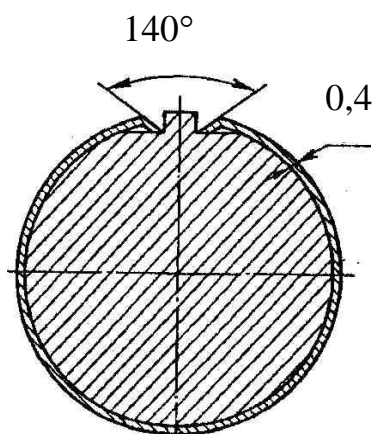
Восстановление шеек коленчатого вала пластинированием
